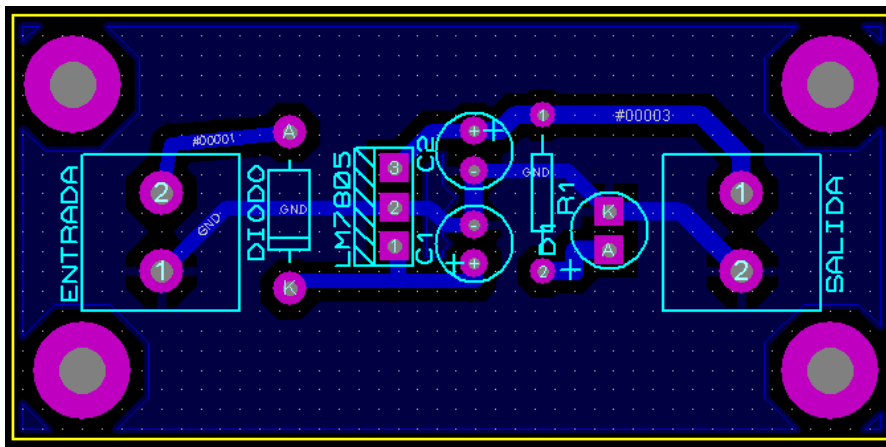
Diseño PCB del circuito del regulador de voltaje
